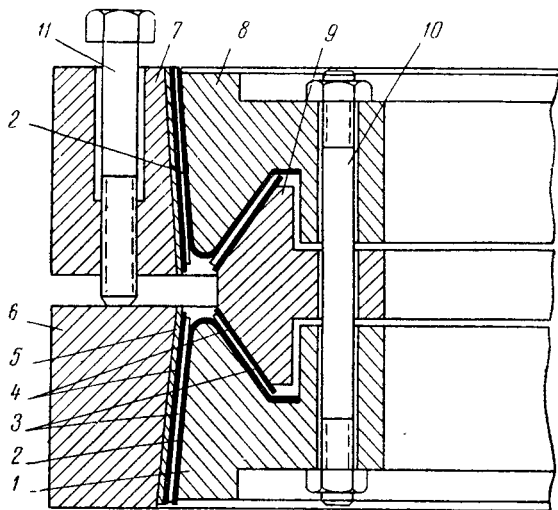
Приспособление для опрессовки и выпечки миканитовых манжет.
